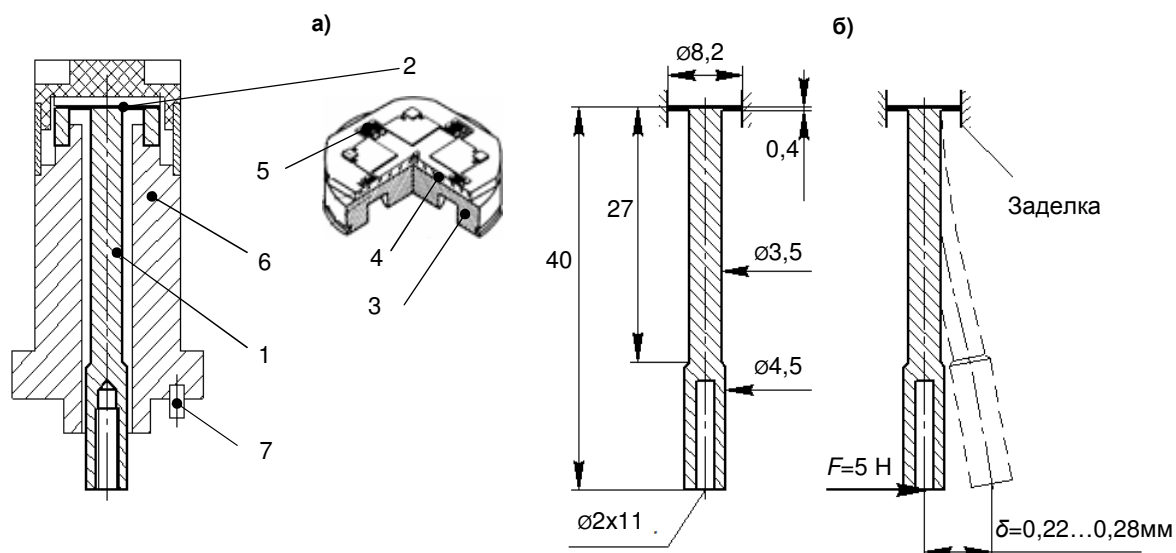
Конструктивная (а) и расчетная (б) схемы тензопреобразователя C05:1 – рычаг; 2 – пластина; 3 – титановый слой; 4 – сапфировый слой; 5 – тензорезистор; 6 – корпус; 7 – установочный штифт
